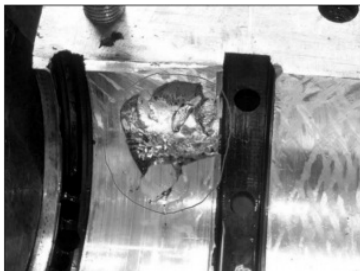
Разрушение баббитового слоя опорного подшипника центробежного нагнетателя ГПА
